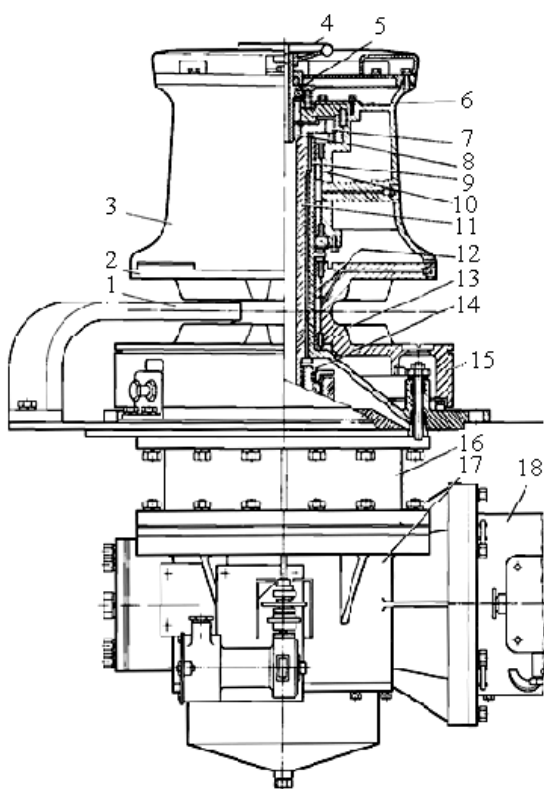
Однопалубный якорно-швартовный шпиль
